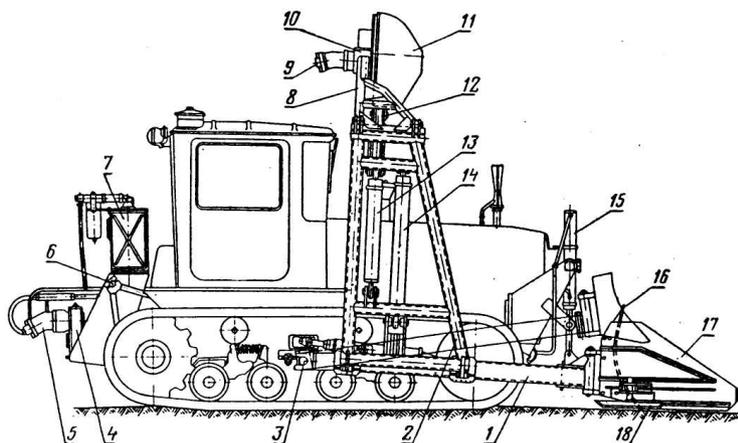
Фрезерный каналочиститель МР-14: 1 — толкающая рама; 2 — рама рабочего органа; 3 — упряжный шарнир; 4 — редуктор; 5 — насос; 6 — базовый трактор; 7 — бак; 8 — рукоять; 9 — гидромотор; 10 — редуктор; 11 — фреза; 12 — гидроцилиндр поворота; 13 — гидроцилиндр подъема; 14 — гидроцилиндр подъема стрелы; 15 — гидроцилиндр подъема отвала; 16 — отвал; 17 — уширители; 18 — лыжа
